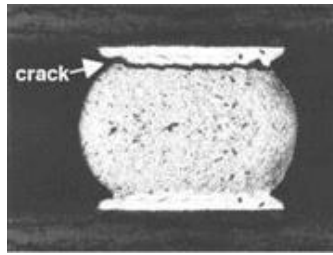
Vue en coupe d'une soudure présentant une fissure s'étant propagée sur l'ensemble de la zone de contact [Lar-03]
